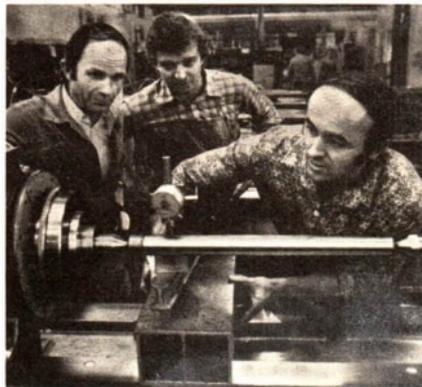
/2 Bearbeitung eines Werkstückes auf einer Drehmaschine
